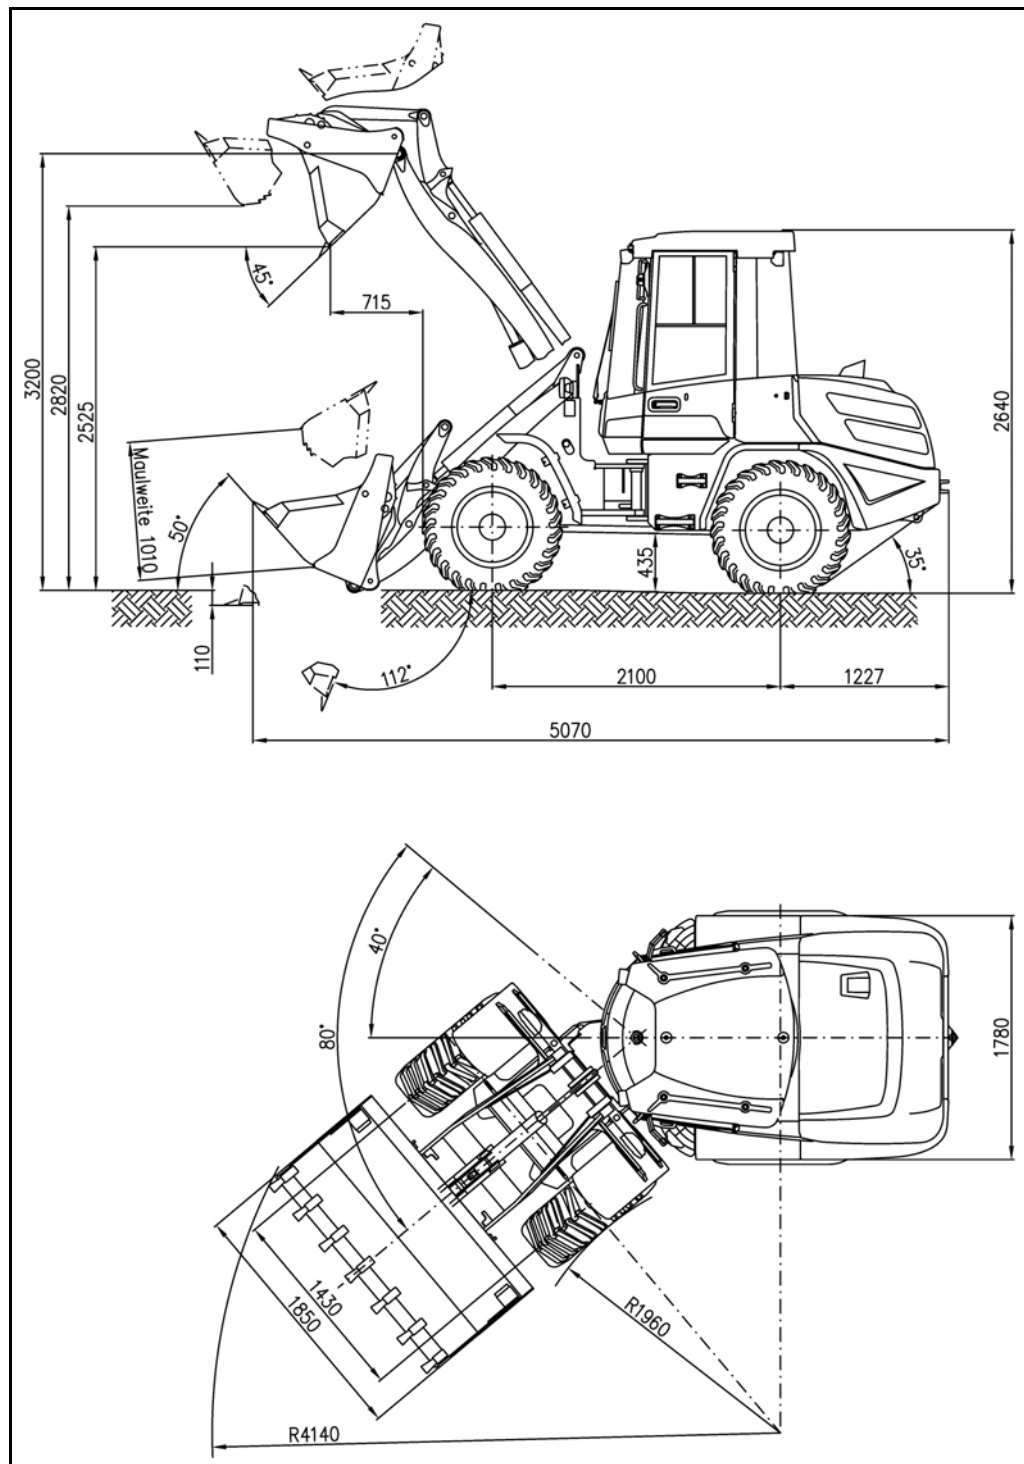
Dimensions - Cinématique parallèle et godet UNI
